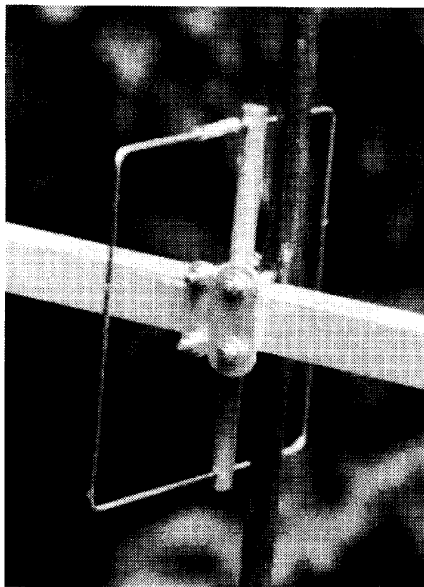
Detail van de twee slotbouten 5 x 35 mm met aluminium plaatje.
